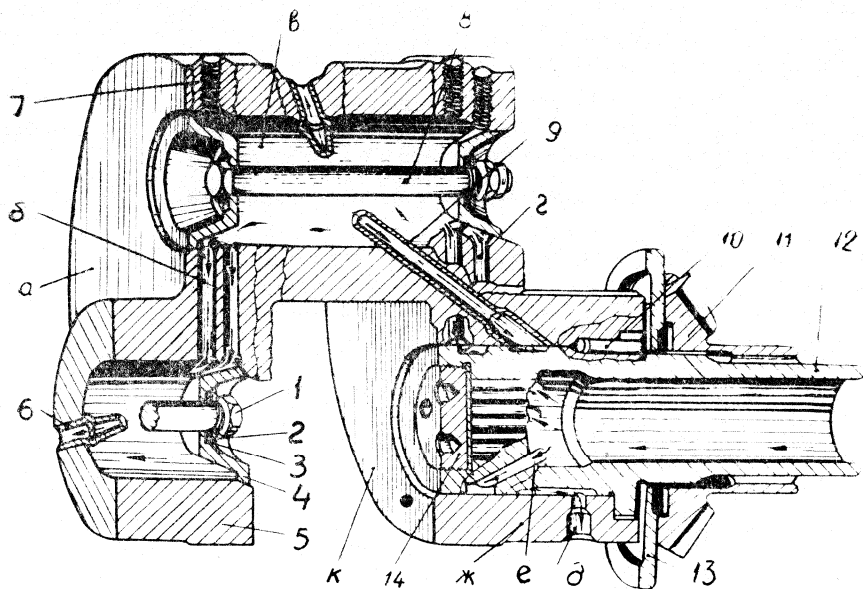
Коленчатый вал. Разрез по первой коренной и шатунной шейкам:
